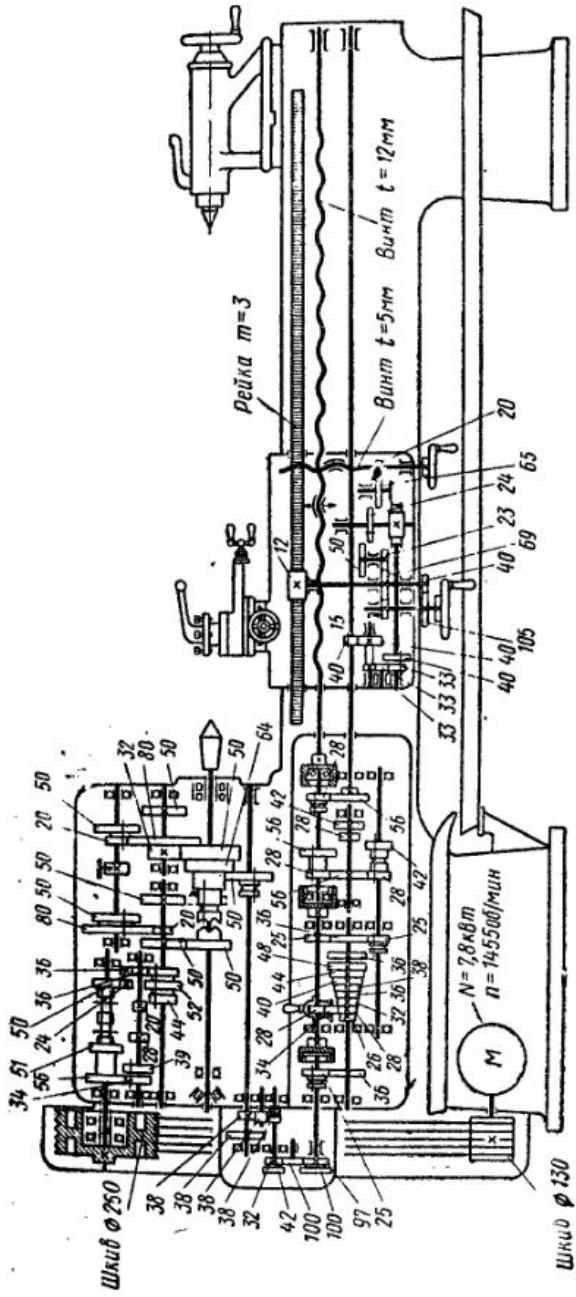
Кинематическая схема станка 1A62 (цифрами обозначены числа зубьев)
